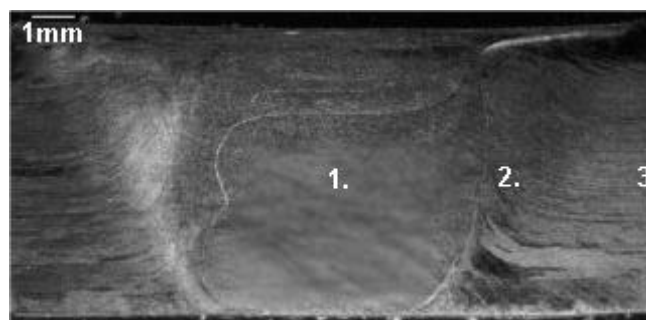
Sección perpendicular a la soldadura: 1) Soldadura 2) Zona de transición, 3) Material base
